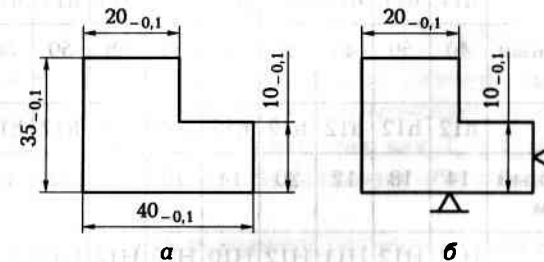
Чертеж детали (а) и схема обработки (б)
